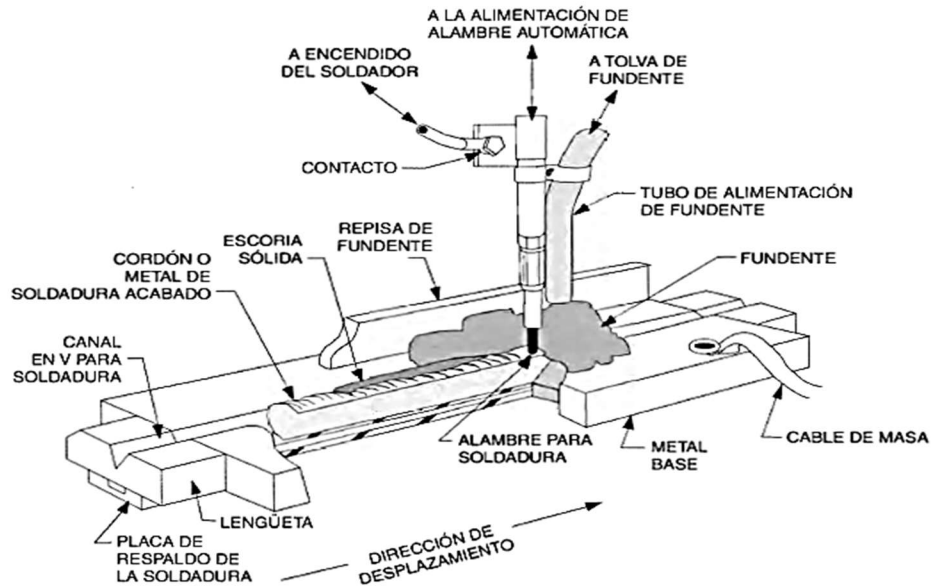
Esquema del proceso de soldadura por arco sumergido (3).
